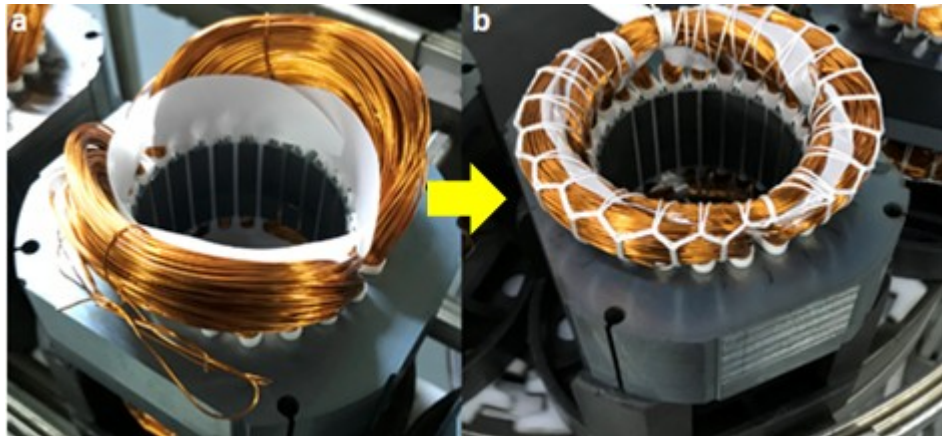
Etapas de fabricação do estator: a) Montagem intermediária; b) Montagem final
